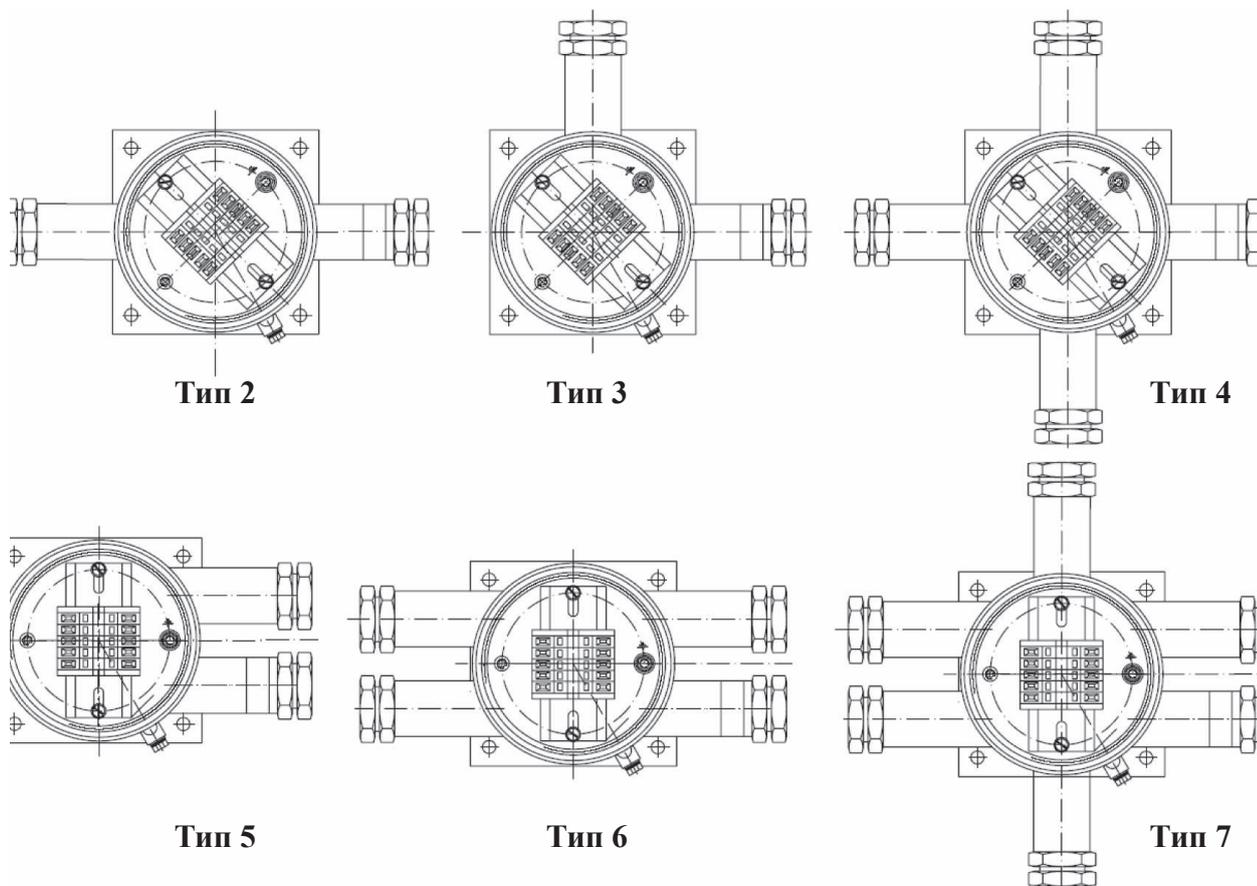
Габаритные, установочные и присоединительные размеры коробок ExКСУВ типов 2–7. Остальные–см. рисунок 1.
